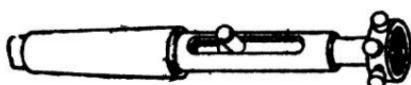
Приспособление со сменными ползунами для нарезания резьбы плашками.
